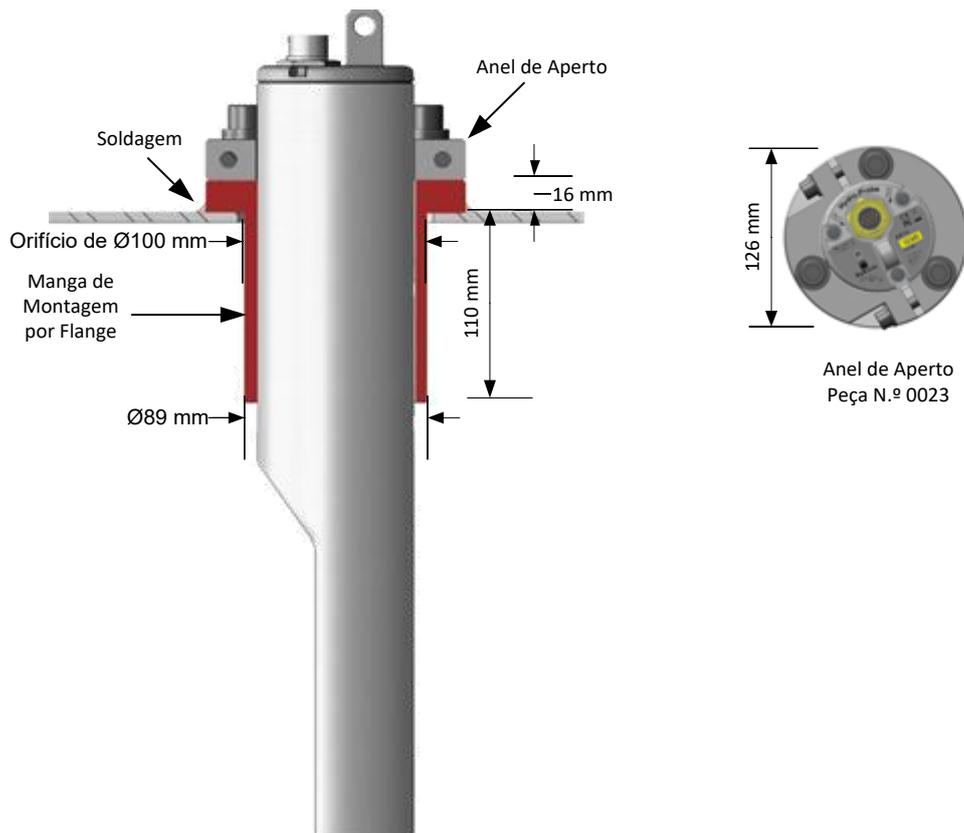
Manga de Montagem por Flange (peça n.º 0024A)
